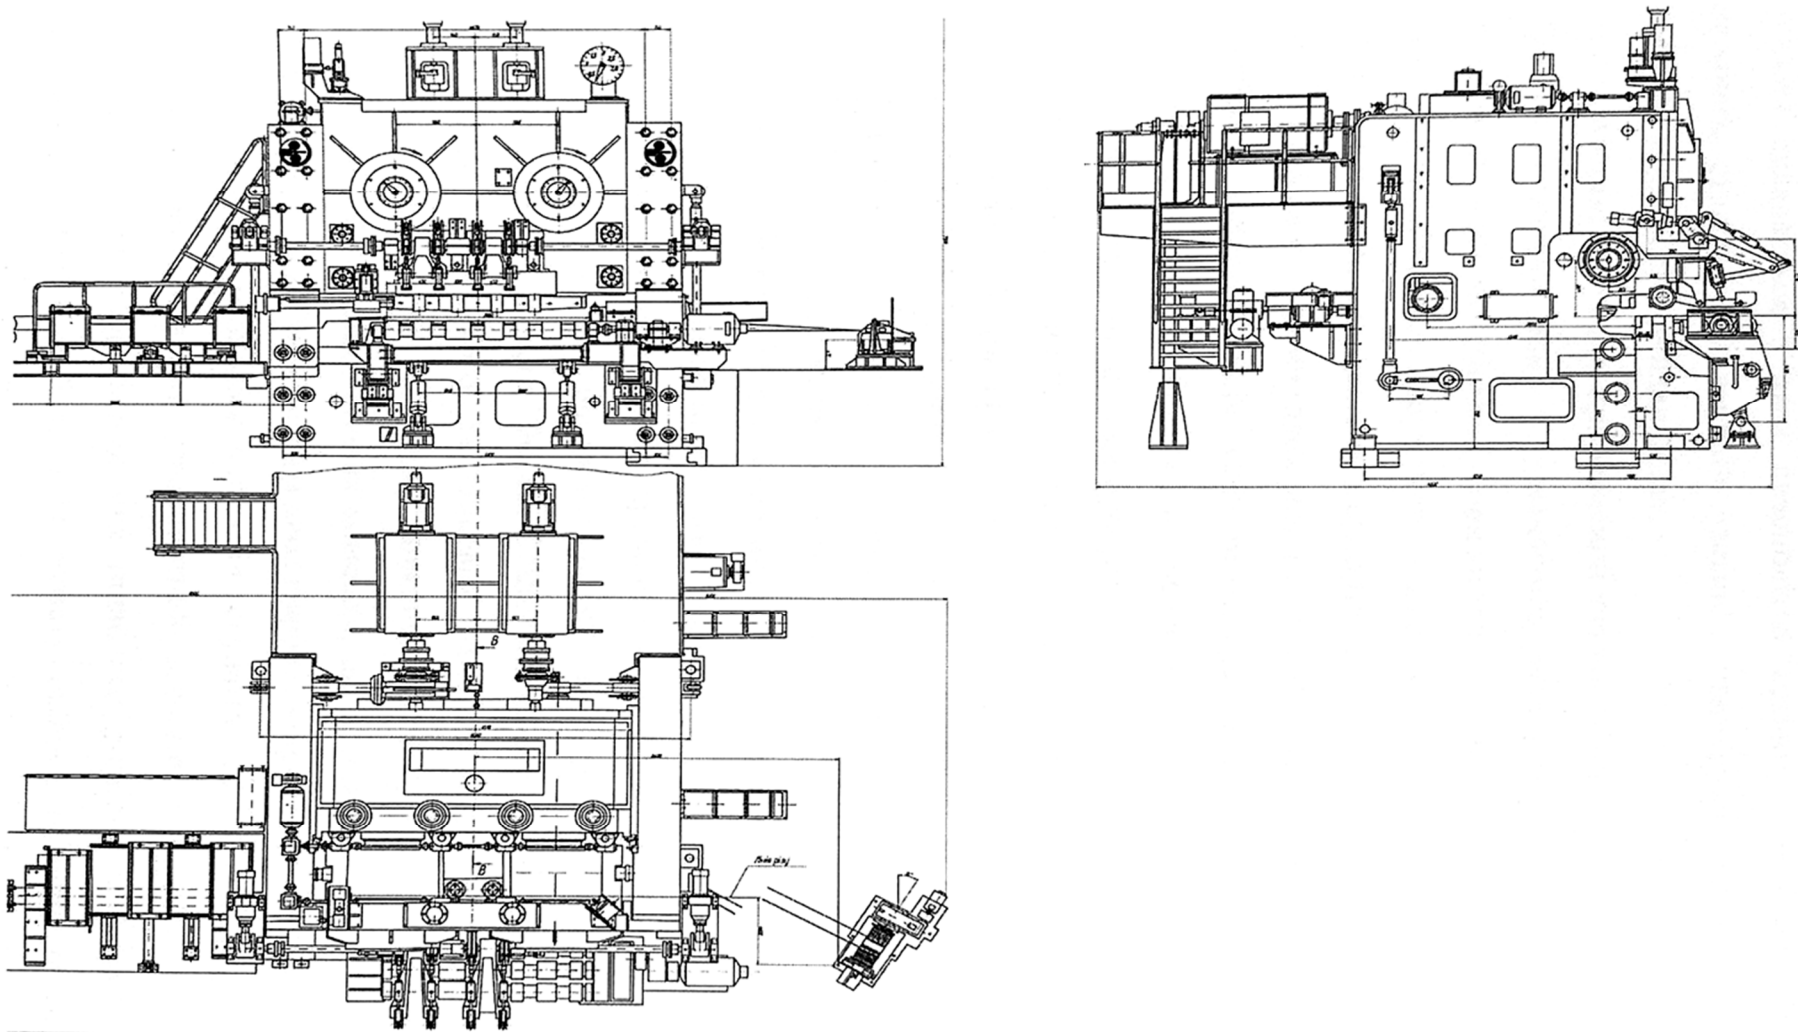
Загальний вид ножиць з перекочуванням різь
